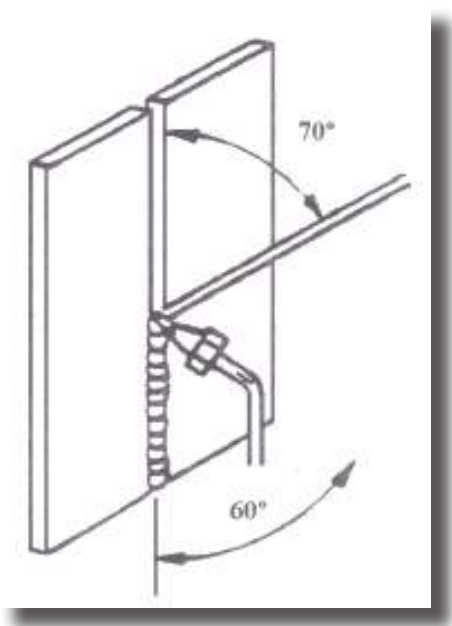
Soldadura ascendente com um único soldador.
